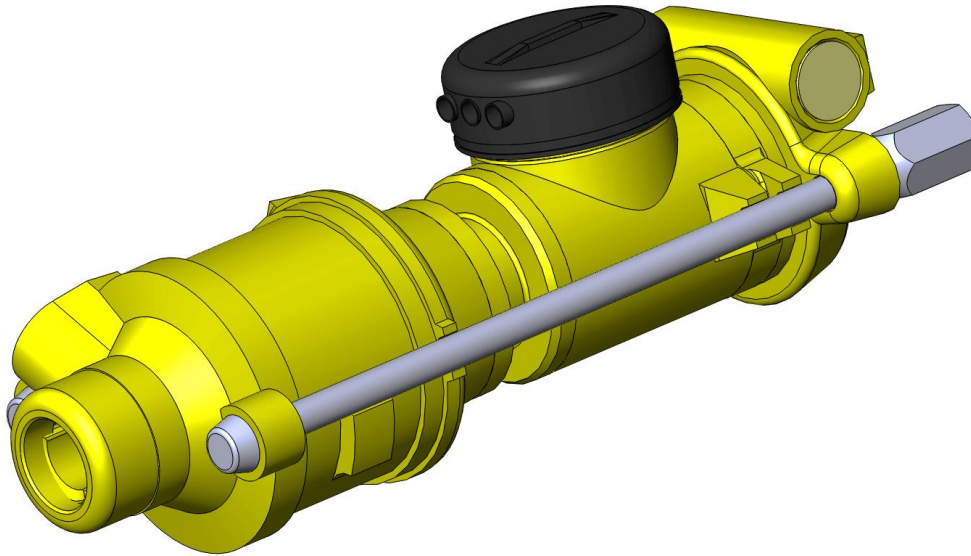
Загальний вигляд колонкового перфоратора ПК-60 [8]
